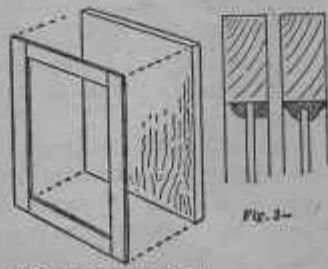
CONSTRUCCIÓN DE LA PUERTA
